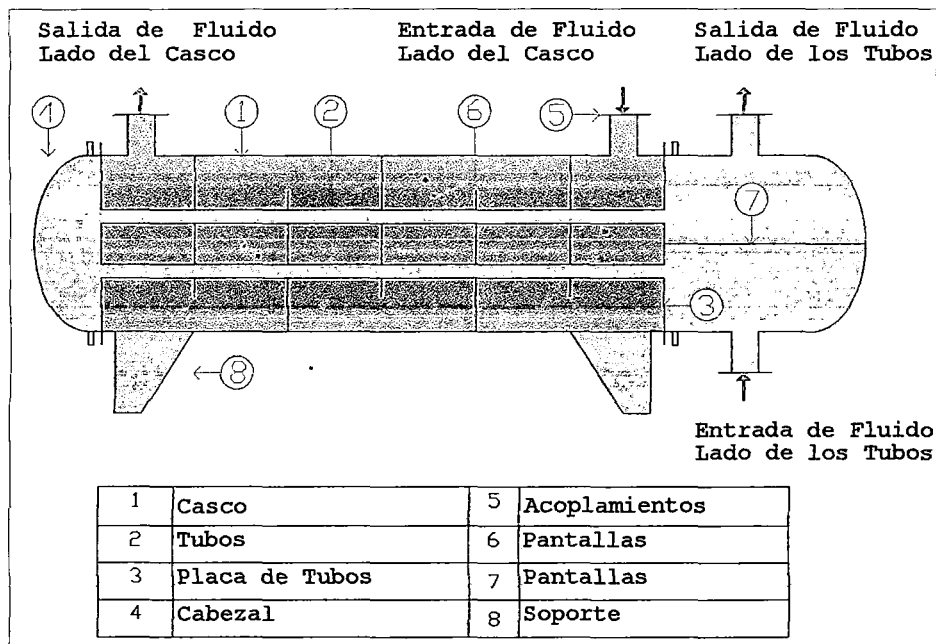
Componentes del intercambiador de carcasa y tubos
